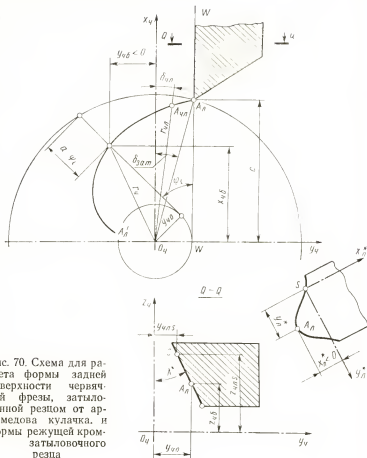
Схема для расчета формы задней поверхности червячной фрезы, затылованной резцом от архимедова кулачка, и формы режущей кромки затыловочного резца
